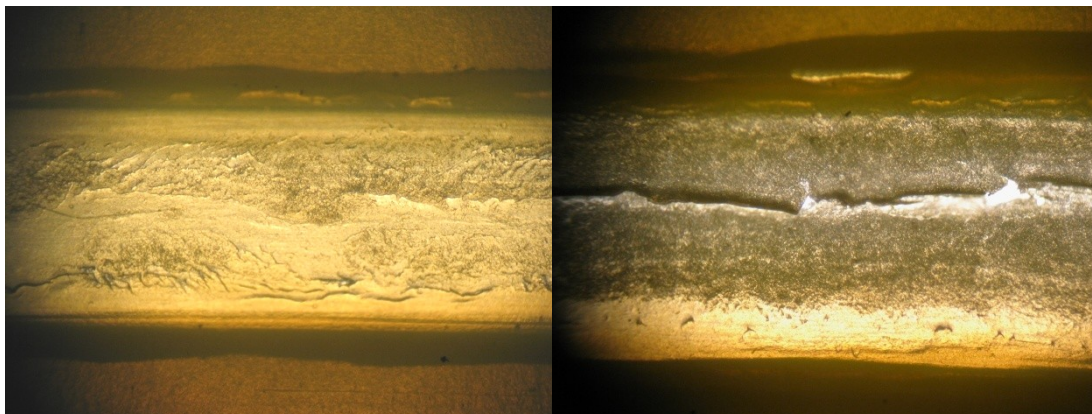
Внешний вид сварного шва листового полиэтилена выполненного УЗ сварочным аппаратом с тиристорным регулятором
